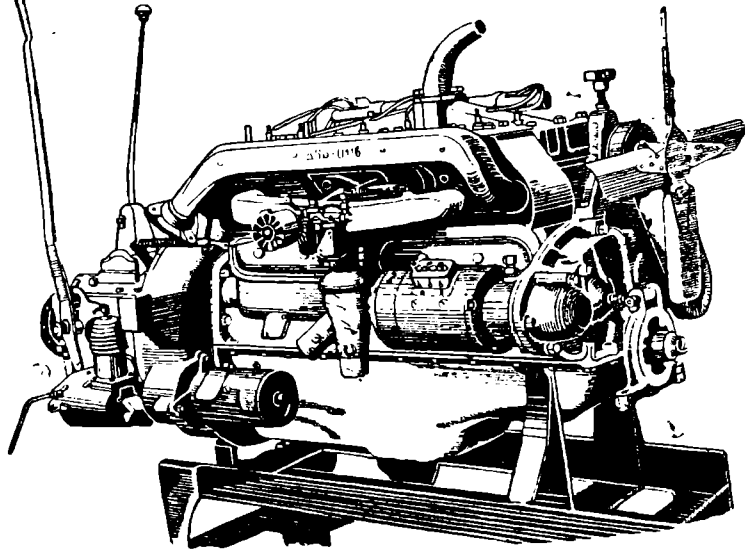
Двигатель ЗИС-21 (вид со стороны смесителя).
